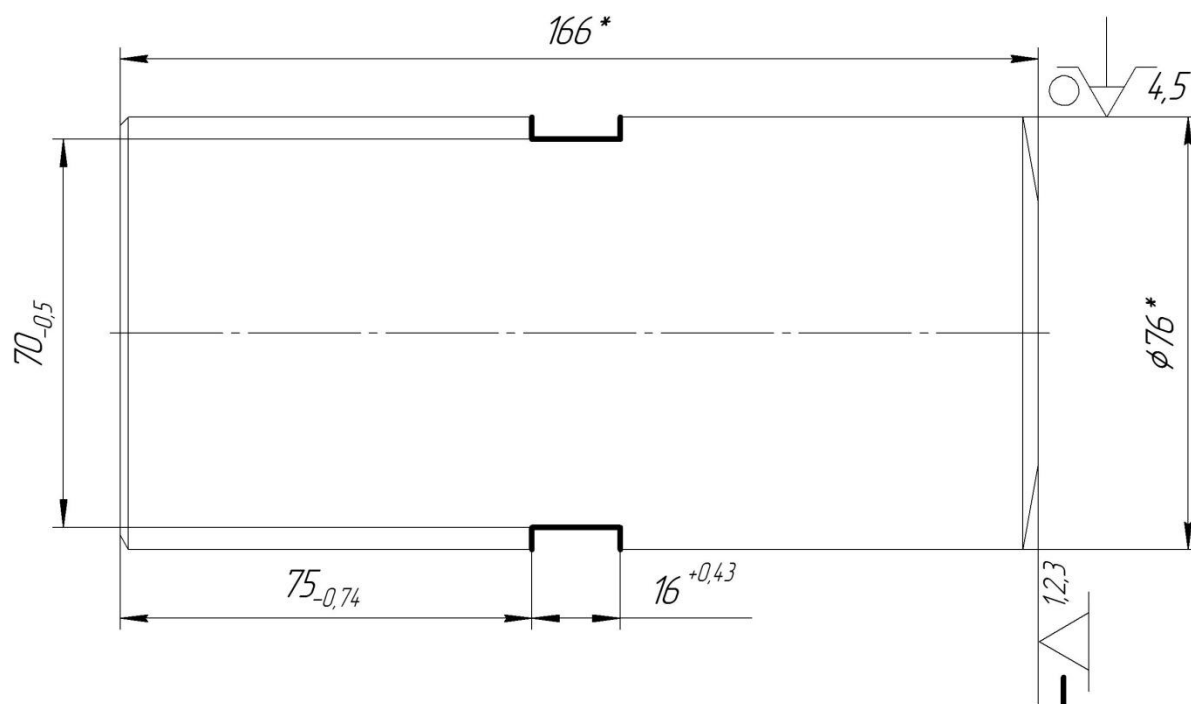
Схема базування заготовки на фрезерній операції (другий варіант)
